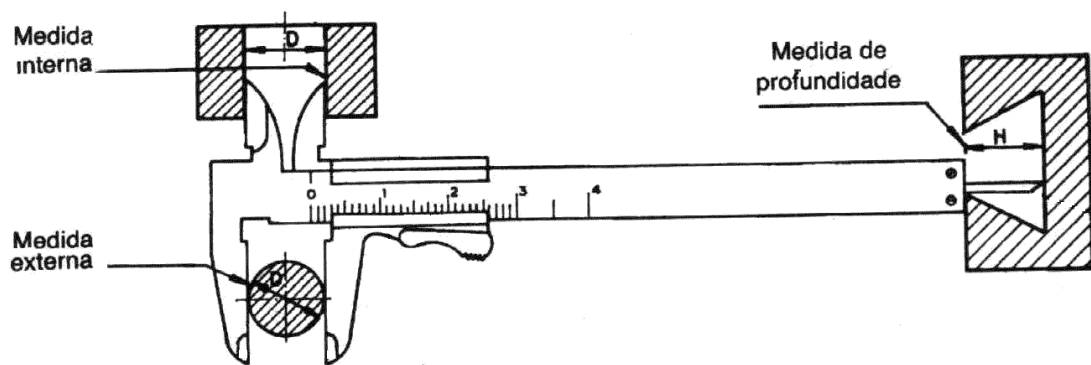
Formas de utilização do paquímetro (Ref. [8])
